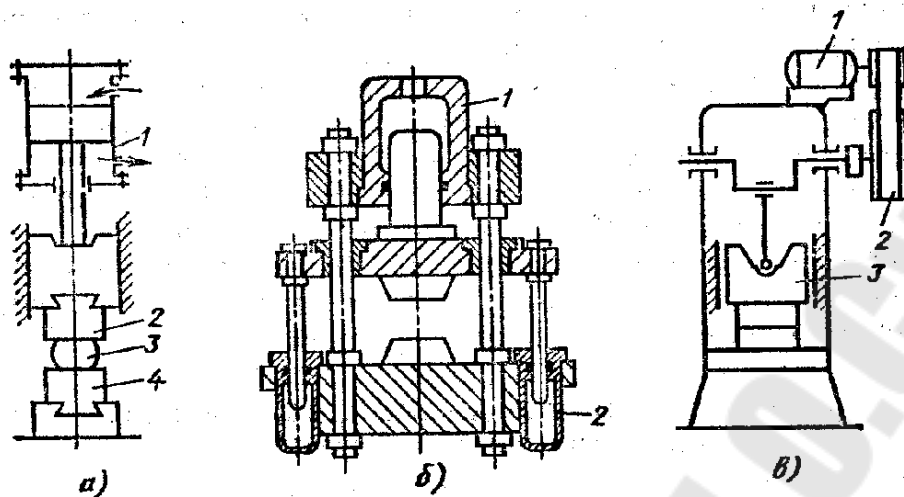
Конструктивные схемы машин для обработки металлов давлением
